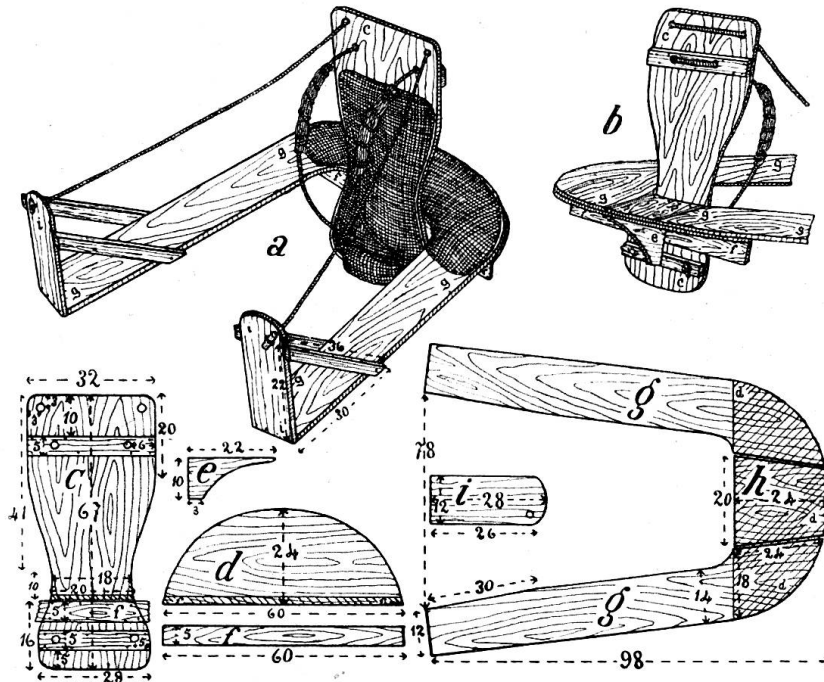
La sellette en U, différentes pièces et manière de les assembler.
